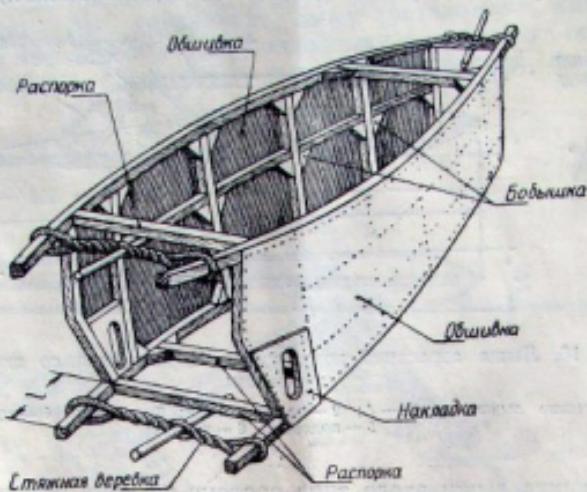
Сборка корпуса аэросаней конструкции Коростылева
